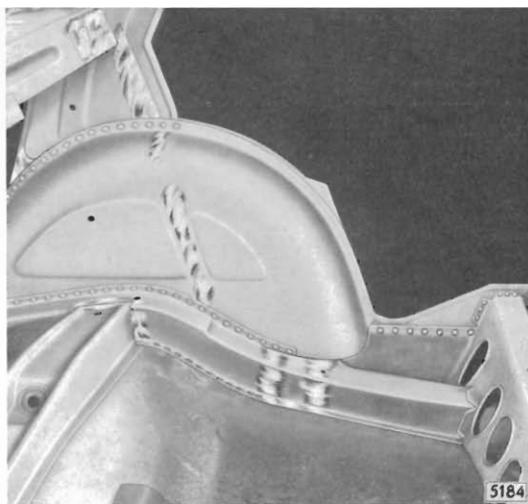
Lichtbogenschweißnaht an der Außenseite des Hinterlängsträgers überschleifen
